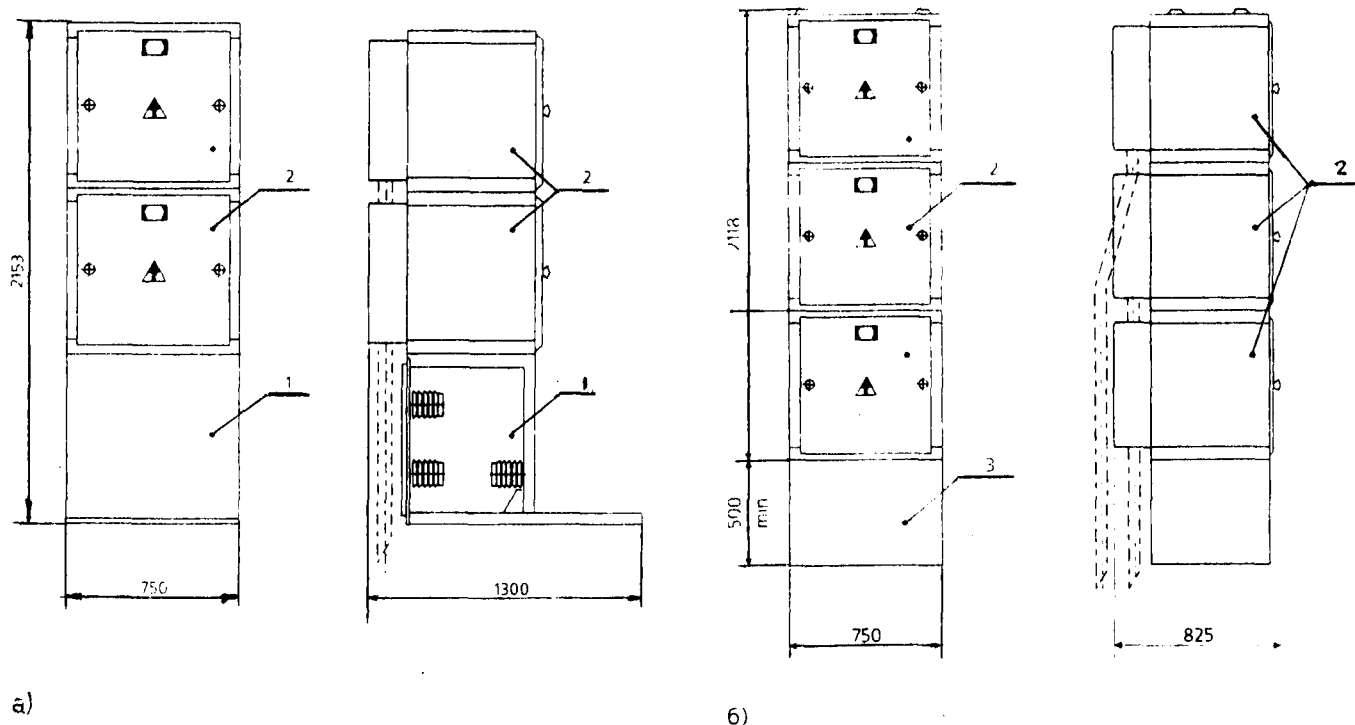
Общий вид и габаритные размеры шкафа серии К-104М с R-C цепями
